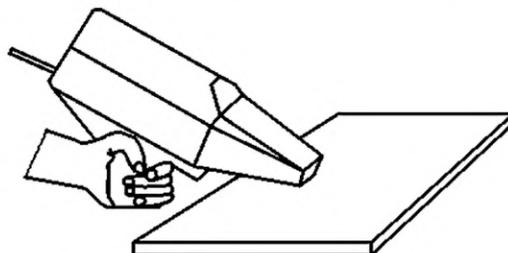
Ручная лазерная обрабатывающая машина (устройство) (лазер является неотъемлемой частью ручной лазерной обрабатывающей машины (устройства)), ручное позиционирование с моторизованной подачей или без нее, заготовка зафиксирована
